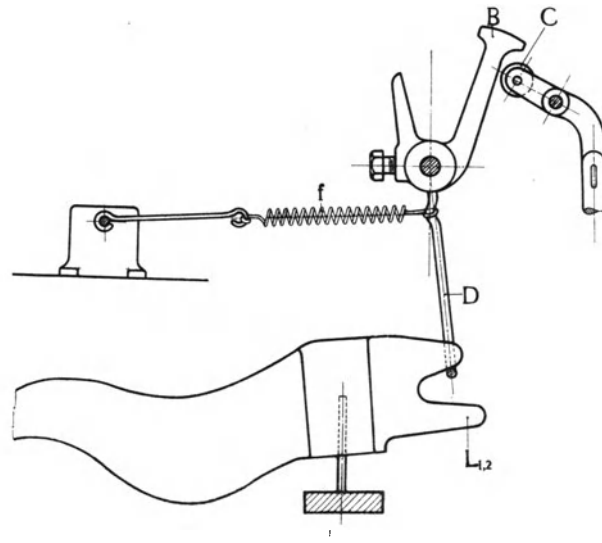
Die Steuerung der Stifthebel durch den Draht D.
